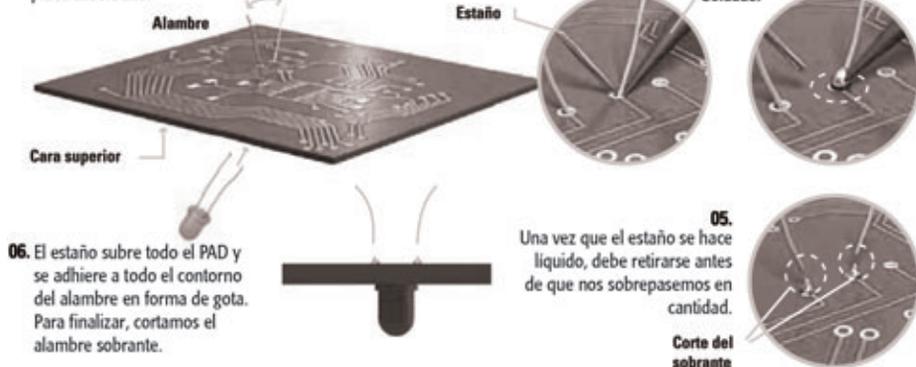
En estos pasos, analizamos cómo realizar el soldado de componentes through hole.
